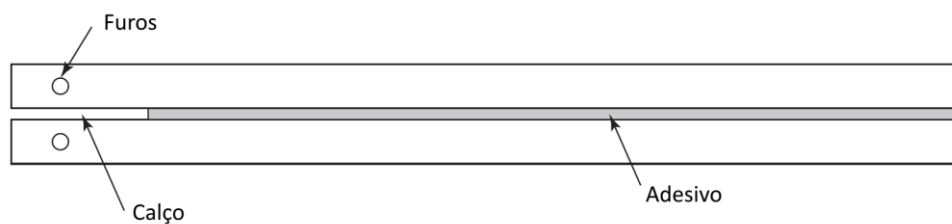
Provete para ensaio DCB (adaptado de[22])
